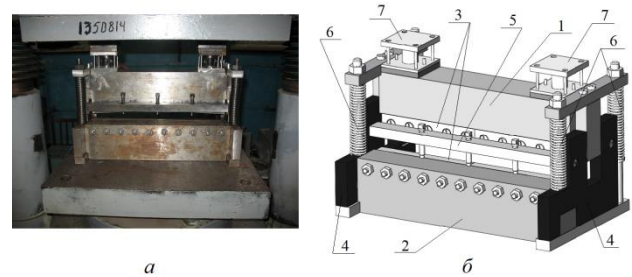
Лабораторные пресс-ножницы: а - общий вид; б - конструктивная схема
